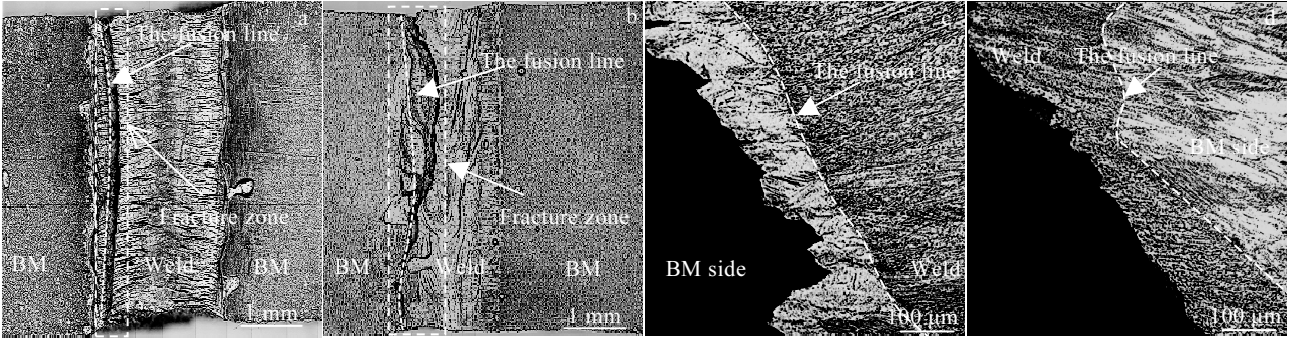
焊接接头拉伸后试样上表面、下表面及横截面形貌
